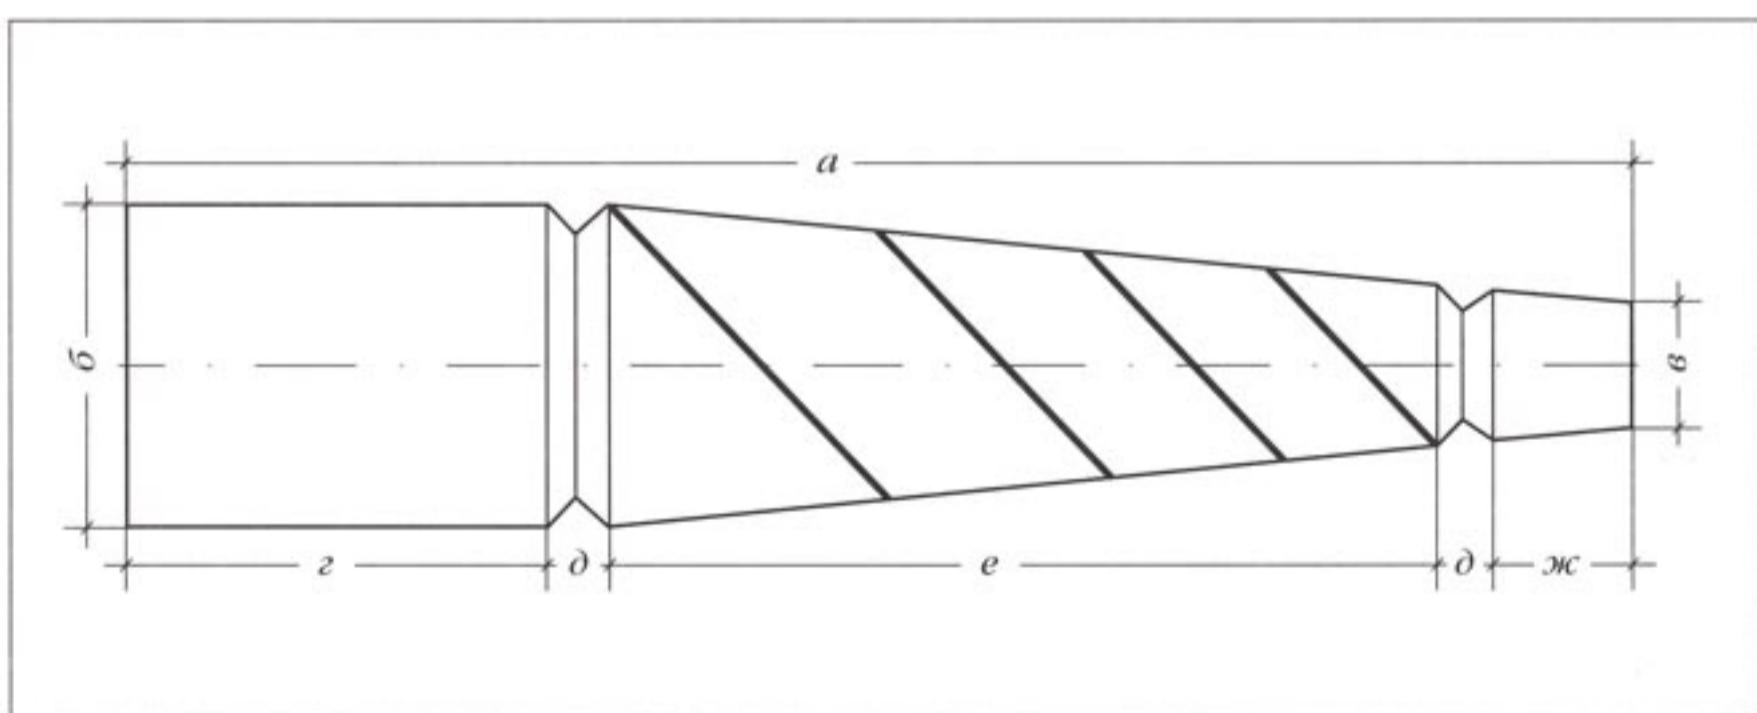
Схема ножки журнального столика с разметкой: а – длина заготовки (45–55 см); б – толщина (размер грани) квадратного бруска (4,5–5 см); в – толщина бруска в конусном окончании (2 см); г – место стыковки деталей стола (10 см); д – прорезное место отрыва винта (5 см); е – место нанесения разметки и прорезки винта; ж – каблучок (его размер должен быть не менее 5 см) для придания ножке большей декоративности (5–7 см)
